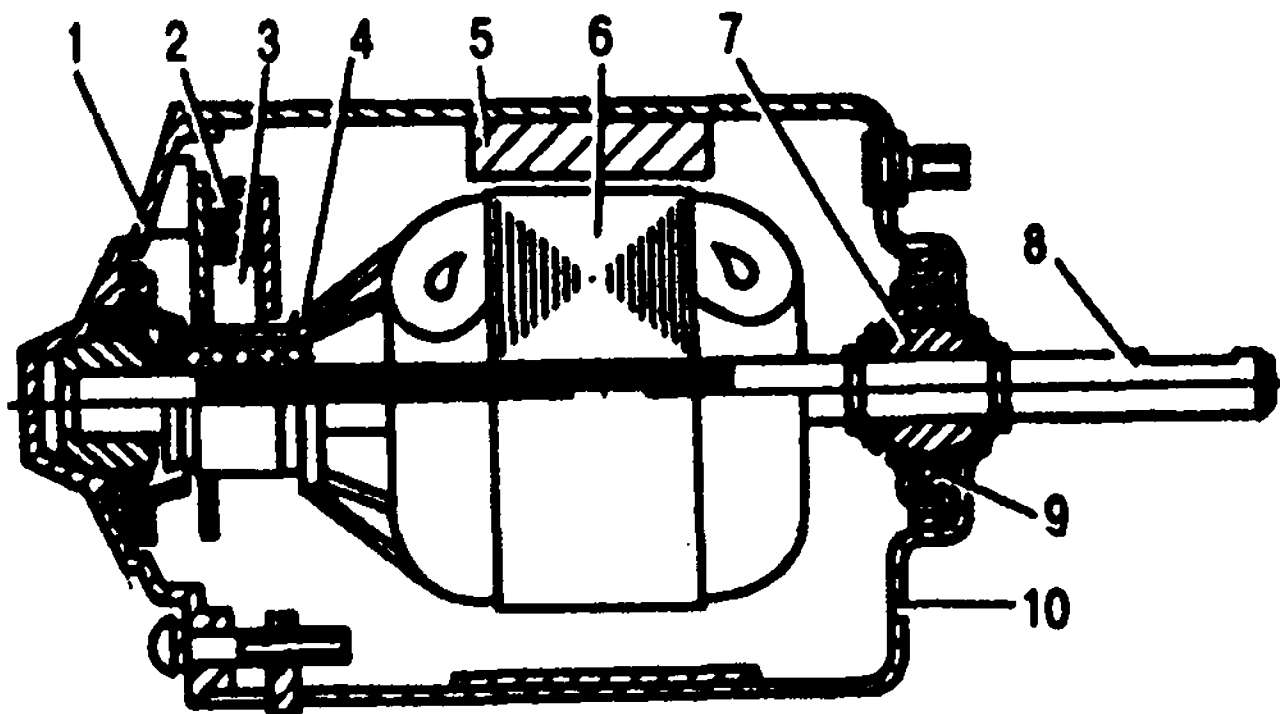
Электродвигатель 194. 3730: 1 - крышка, 2 - пружина, 3 - щетка, 4 - коллектор, 5 - постоянный магнит, 6 - якорь, 7 - подшипник, 8 - вал, 9 - фетровая шайба, 10 - корпус
